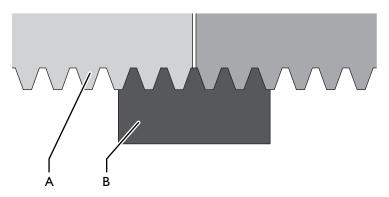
Montagehilfe für Zahnstangenmontage
